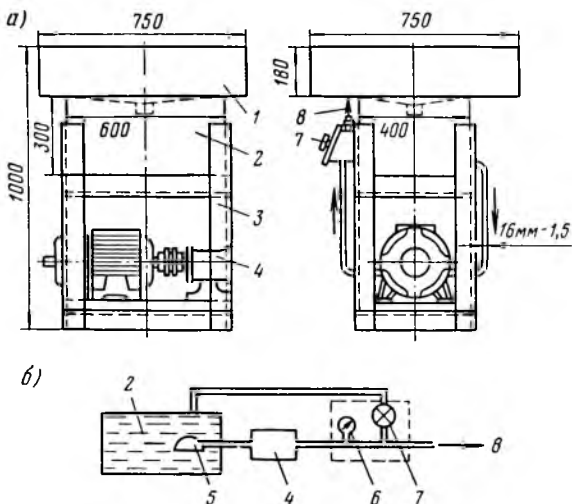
Стенд для проверки узлов гидромеханической передачи на герметичность:
